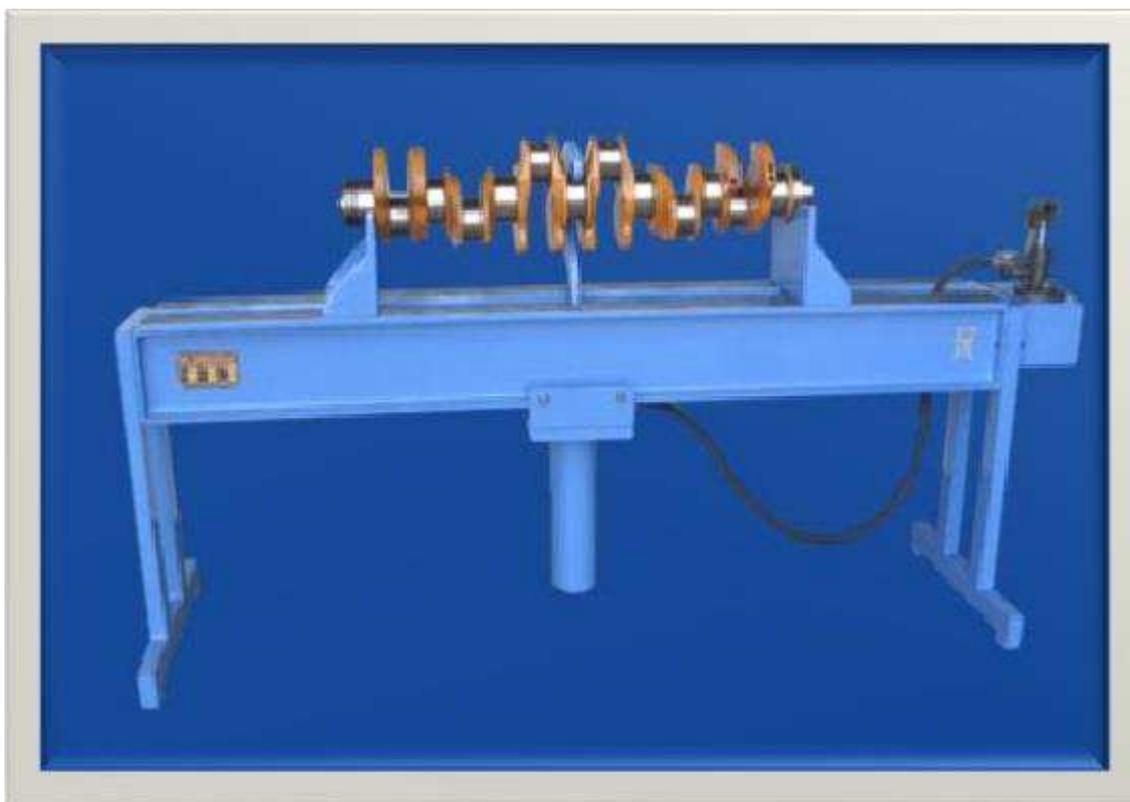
Гидравлический пресс для правки коленвалов KDP 1800
